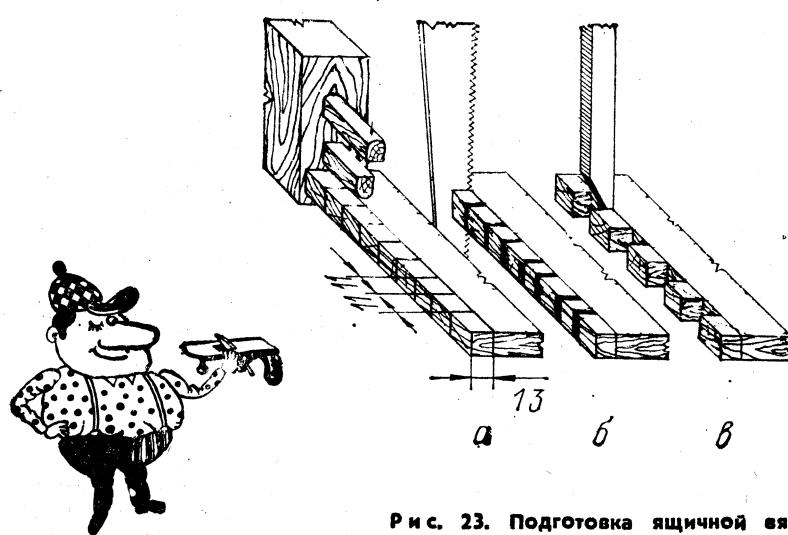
Подготовка ящичной вязки: а — разметка рейсмусом; б — запиливание шипов; в — выдалбливание проушины
